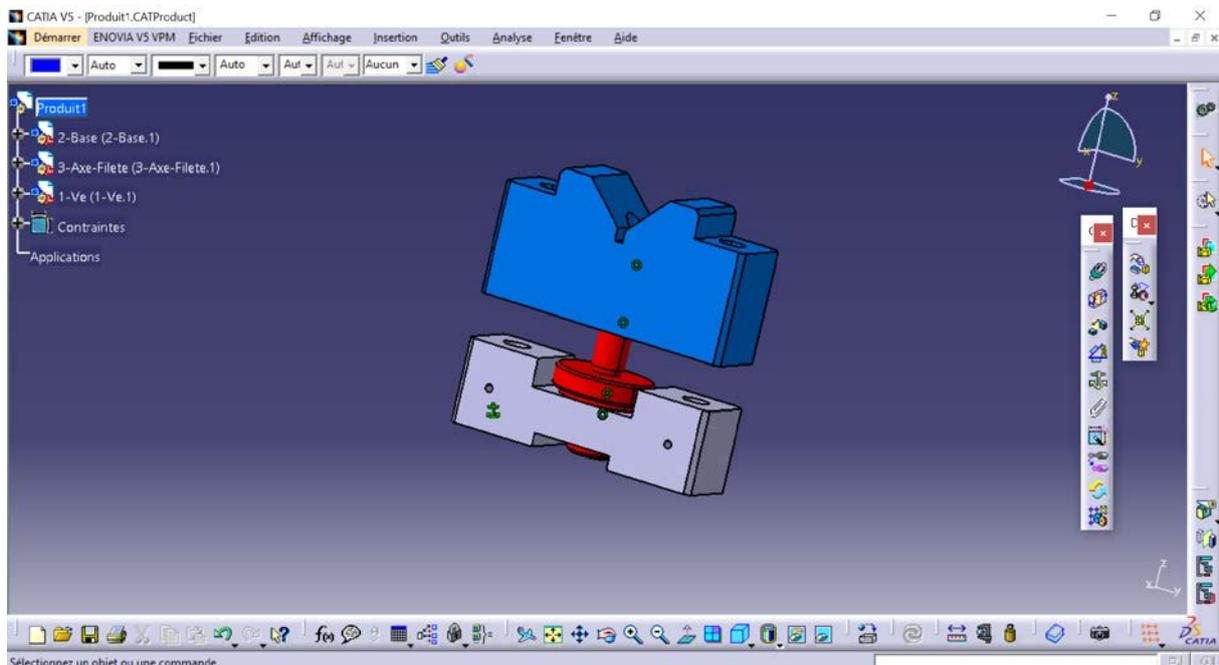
Assembly Design des Pièces 1, 2 et 3 [1], [2]
